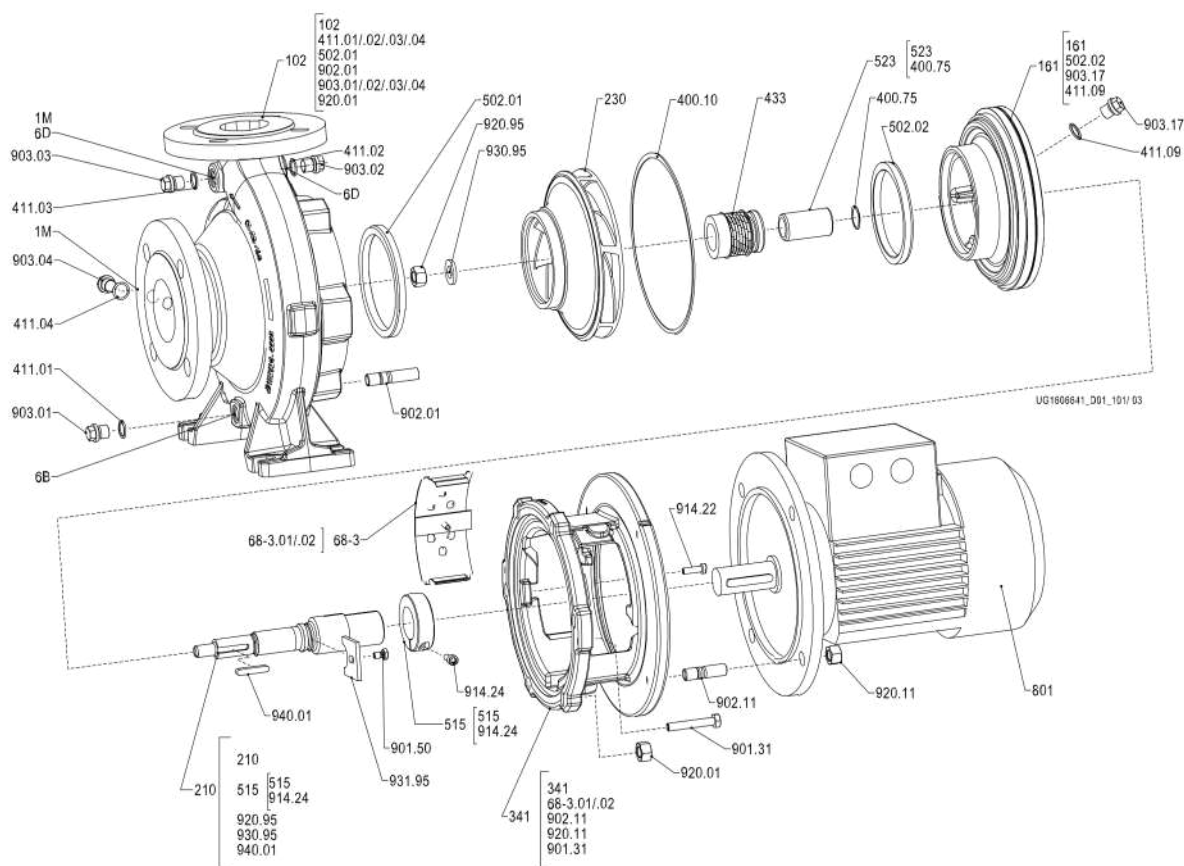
Modelo con cierre mecánico simple y tapa de la carcasa encajada, con pie de bomba
